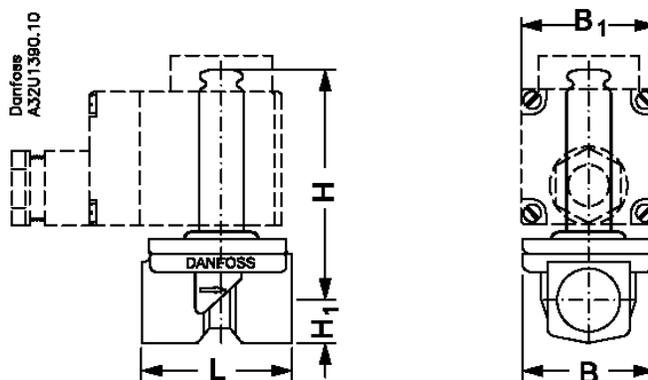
Габаритные и присоединительные размеры соленоидного клапана.
